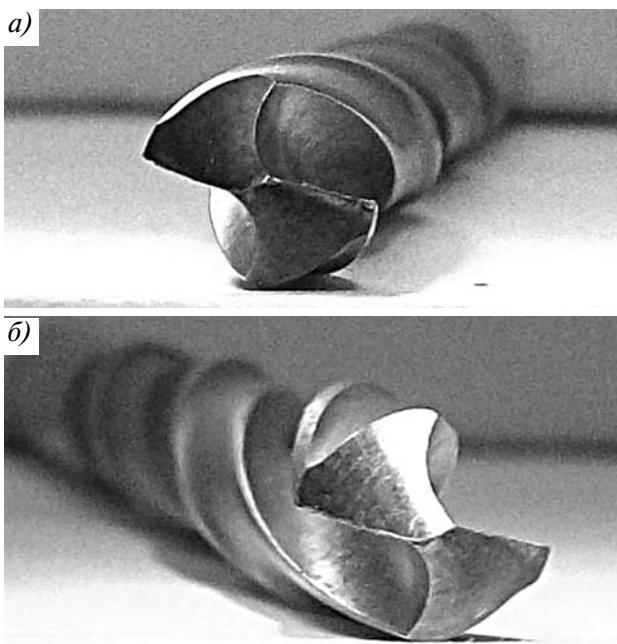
Износ задней поверхности главной режущей кромки из стали Р6М5:
